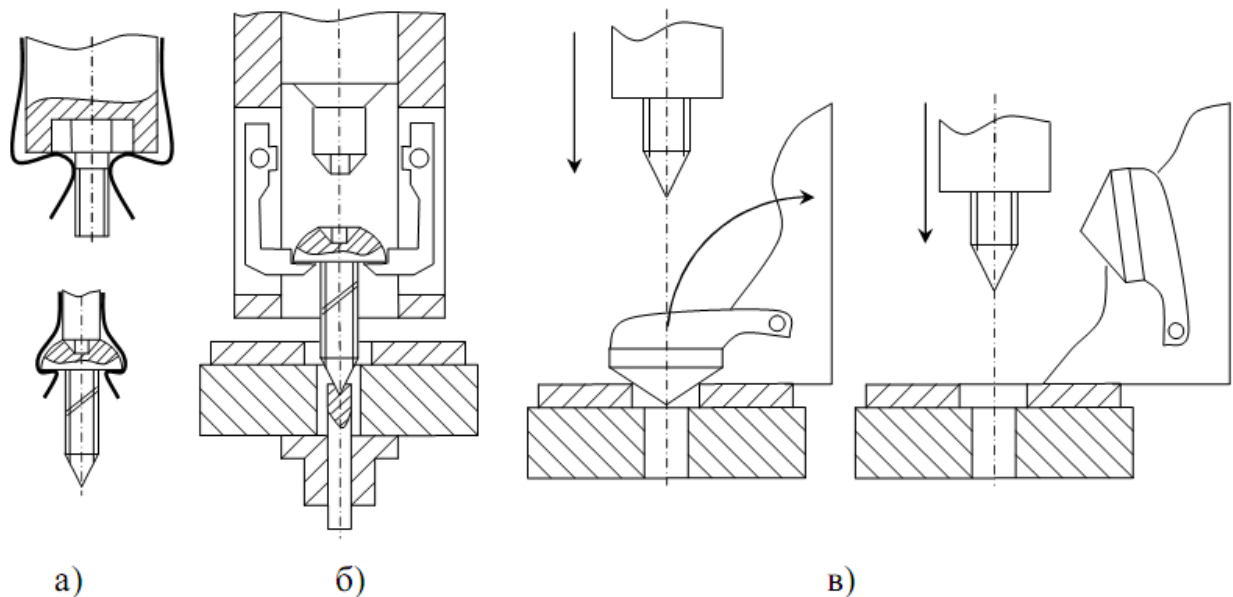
Схеми базування гвинтів в початковий момент загвинчування:
